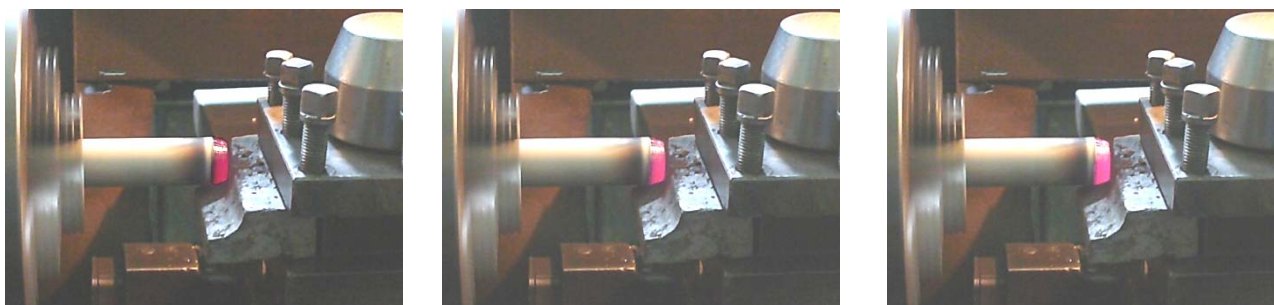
Вид заготовки, нагретой до температуры 600, 800 и 900 °С
